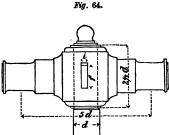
geschmiedeter Kreuzkopf für Balanciermaschinen.
